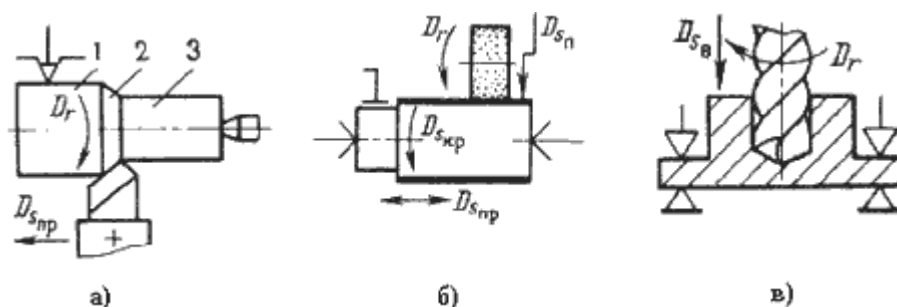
Схемы обработки заготовок: а – точением; б – шлифованием на круглошлифовальном станке; в – сверлением
